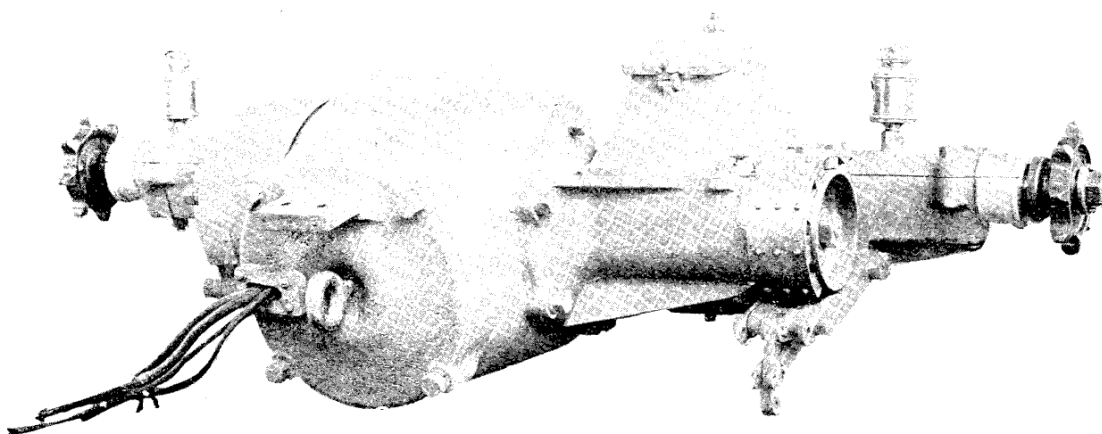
Vue d'ensemble du moteur V2 avec son arbre intermédiaire.
